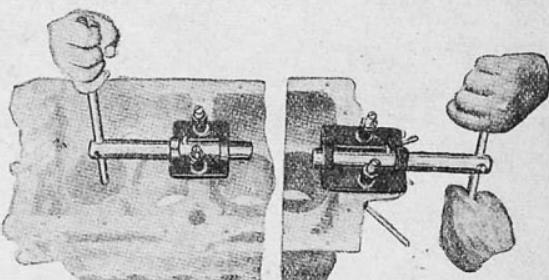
Процесс нарезки смазочных канавок коренных подшипников
